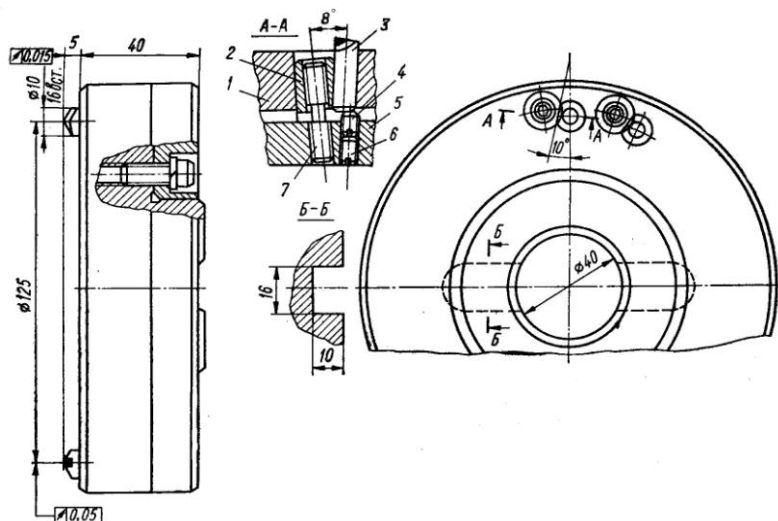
Схема багатозубої торцевої фрези конструкції ВНДП
